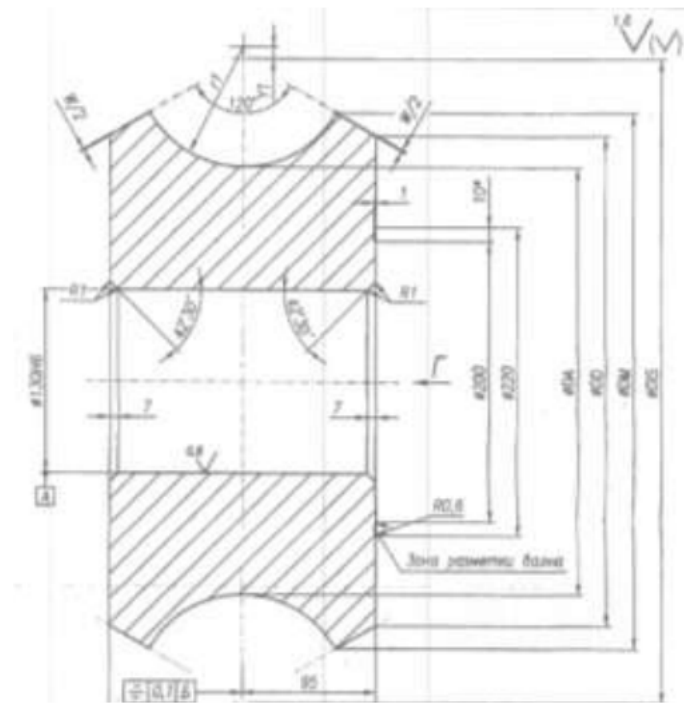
Общий вид отливки «Трубопрокатный валок» из чугуна ТШХН-50 [1]
